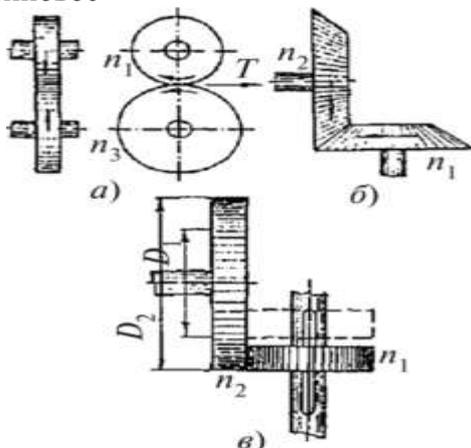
Фрикционные передачи с цилиндрическими (*a*) и коническими (*б*) колесами и торцовый вариатор (*в*)
